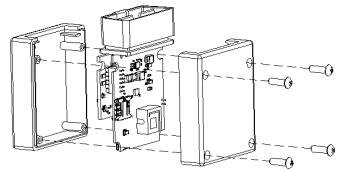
Вскрытие корпуса терминала (310 — слева; 312 — справа; 311 -снизу)
